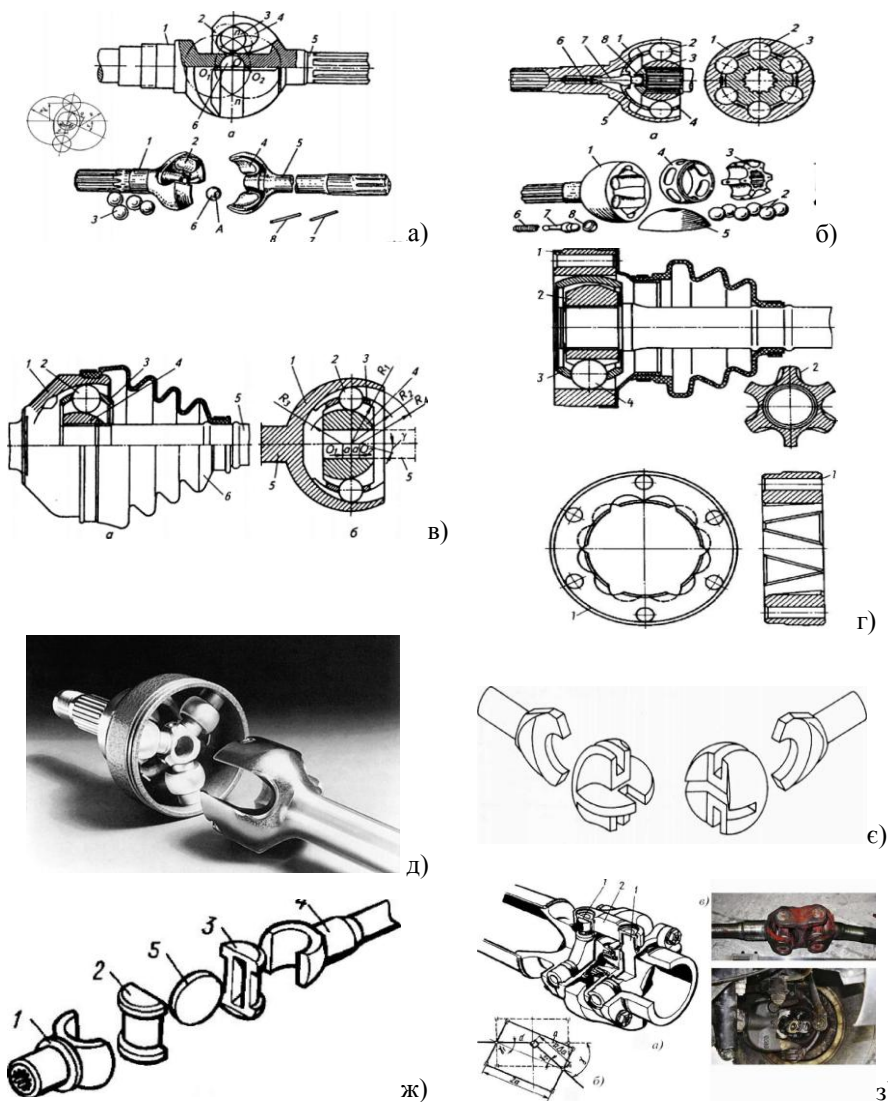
Шарніри рівних кутових швидкостей: а) - чотирикульковий карданний шарнір з ділильними канавками (типу «Вейсс»); б) - шестикульковий карданний шарнір з ділильним важільцем «Рцеппа»; в) - шестикульковий карданний шарнір з ділильними канавками (типу «Бірфільд»); г) - шестикульковий карданний шарнір з ділильними канавками типу «Лебро»; д) - тришиповий шарнір типу «Трипод»; е) – кулачковий шарнір «Тракту»; ж) - кулачково-дисковий шарнір; з) - здвоєний карданний шарнір.
